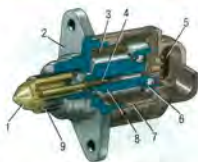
Регулятор холостого хода двигателя K4M: 1 – клапан; 2 – корпус регулятора; 3 – обмотка статора; 4 – ходовой винт; 5 – штепсельный вывод обмотки статора; 6 – шариковый подшипник; 7 – корпус обмотки статора; 8 – ротор; 9 – пружина
